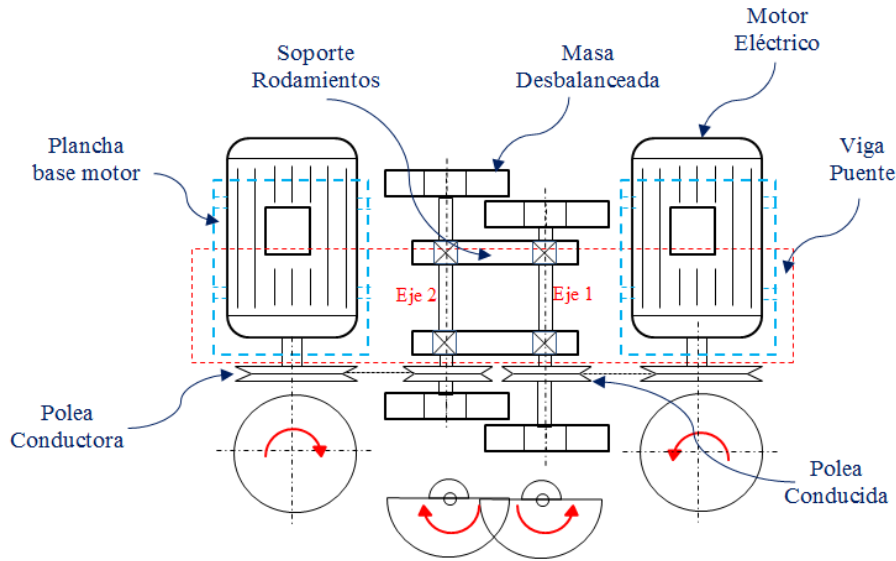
Disposición del sistema de excitación en la viga puente.
